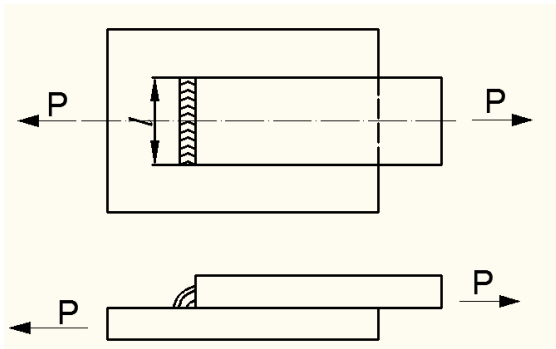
Розрахункова схема напусткового зварного з'єднання з лобовим швом
